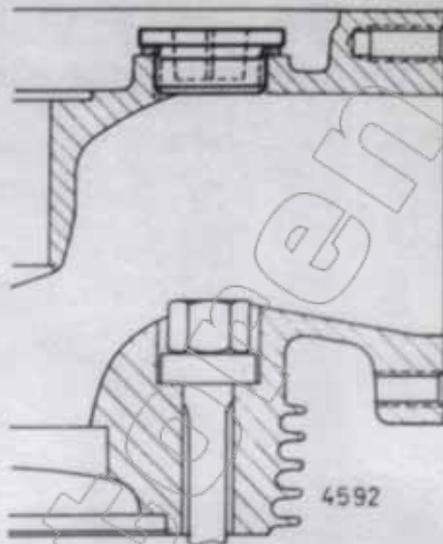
Verschlusschraube zu den Senkbohrungen für die Zylinderkopfschrauben
